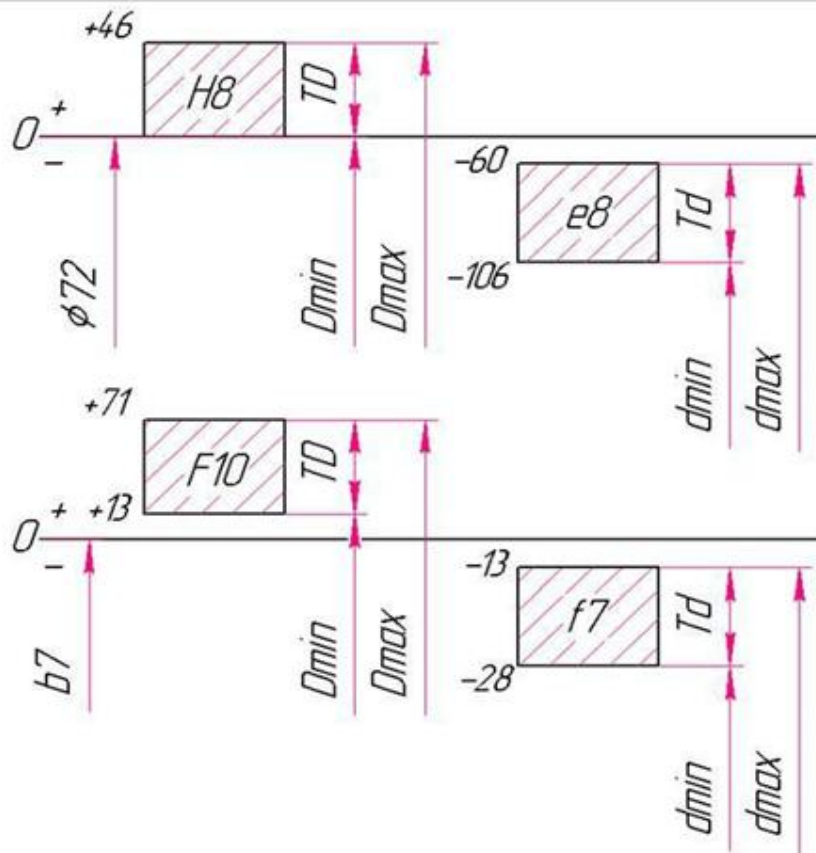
Схема полей допусков шлицевого соединения.
